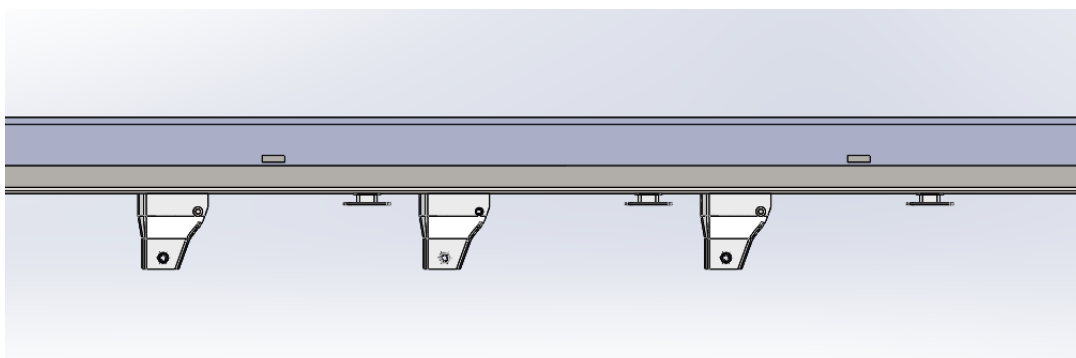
Colocación de handbrackets y soporte de fuelles.
